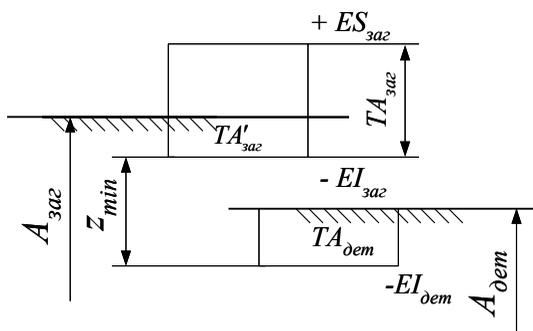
Расчетная схема для определения размера заготовки с учетом закона копирования погрешностей (охватываемый размер детали)
